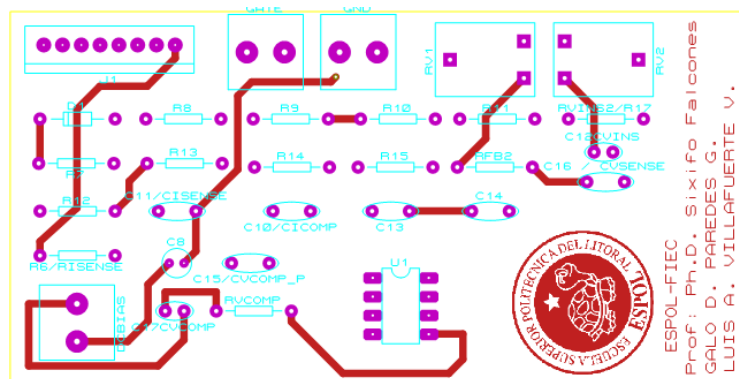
Cara frontal del PCB del circuito de control, prototipo final.
